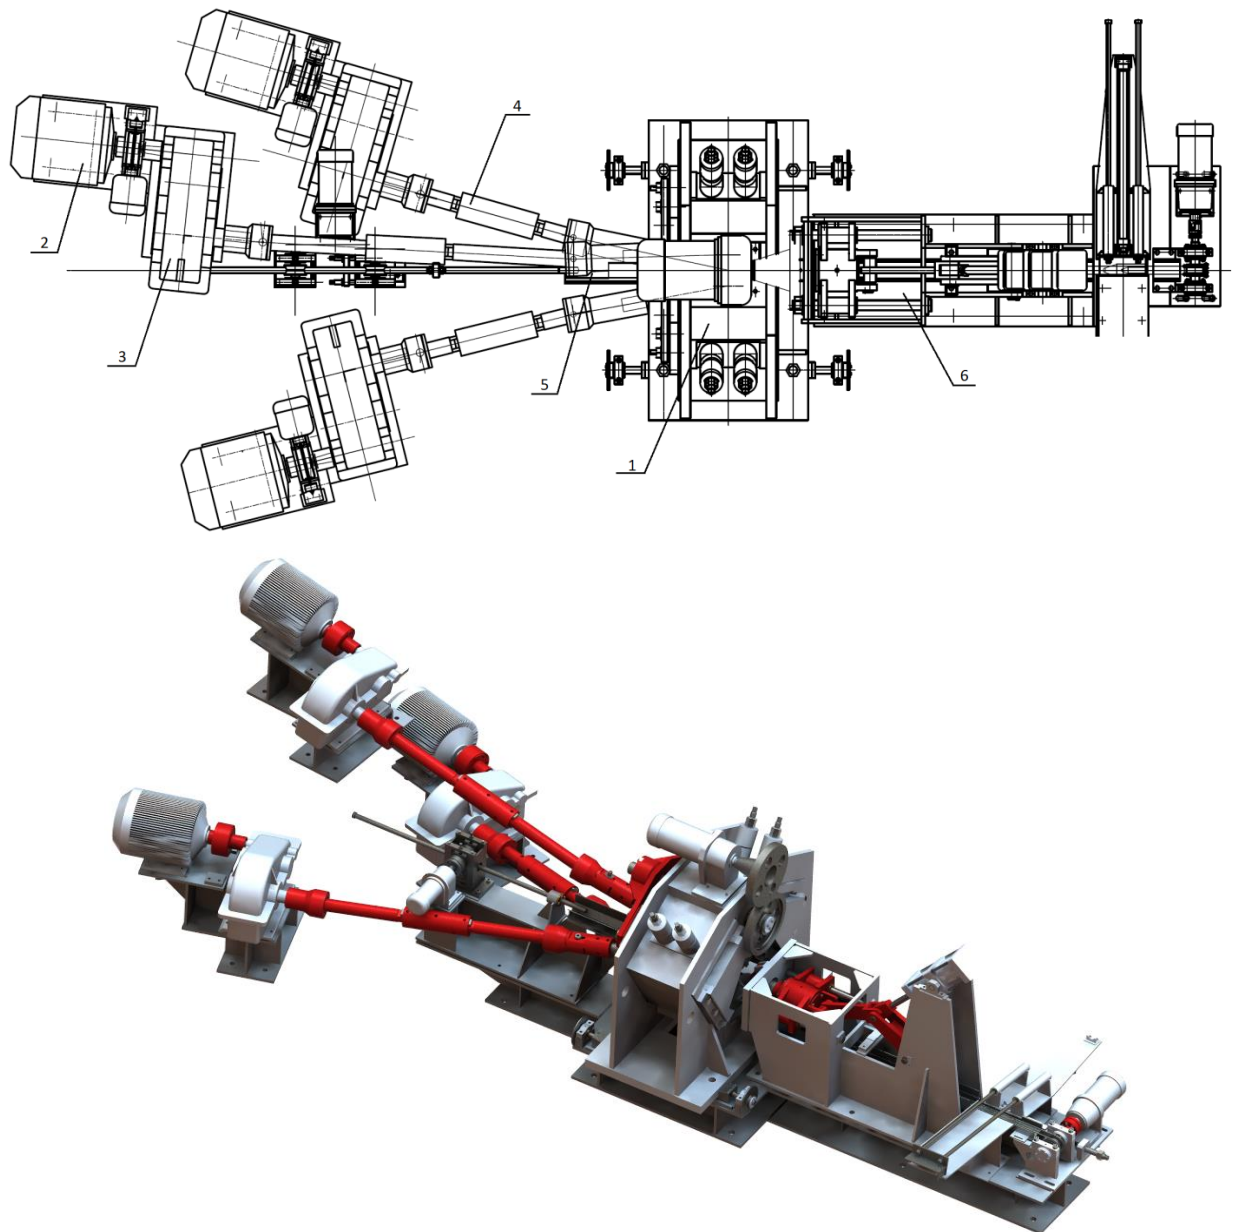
Трехвалковый прошивной стан «30-80»: 1 – рабочая клеть;
